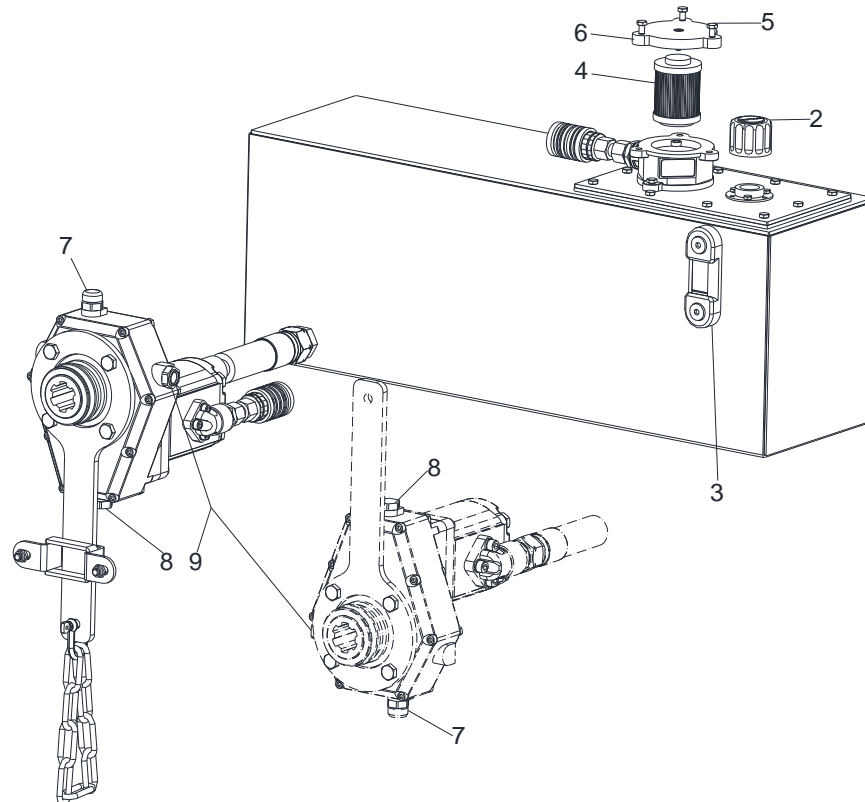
Externe Ölversorgung DS1200, DS1600, DS3100
